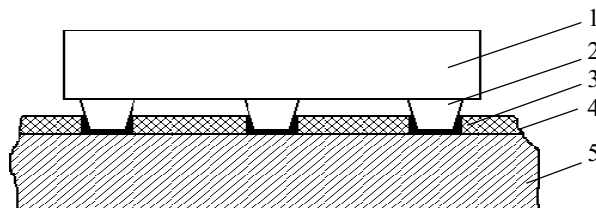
Установка бескорпусного кристалла с объемными выводами на плату:
